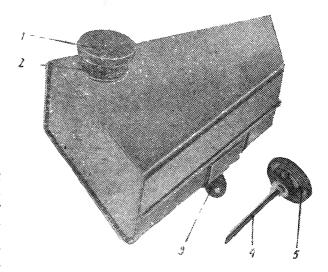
Топливный бак: 1 — пробка; 2 — горловина; 3 — ушко; 4 — мерная линейка; 5 — уплотнительная прокладка
